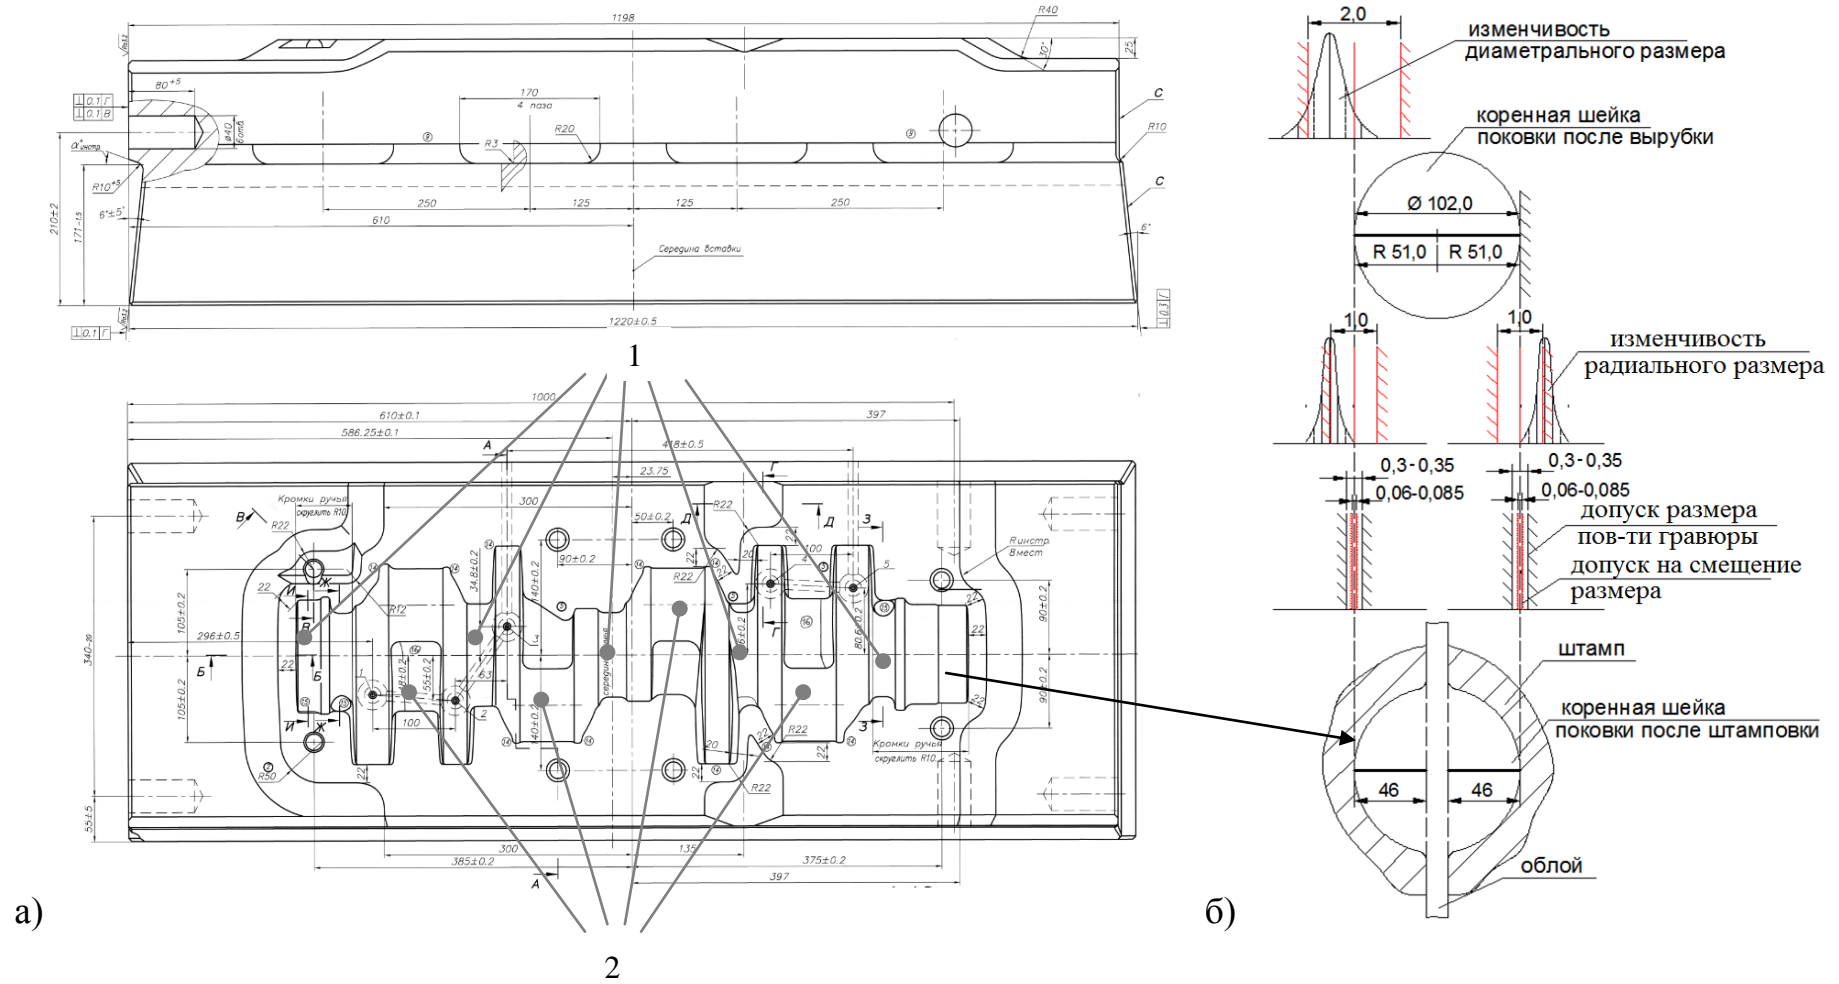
а) Нижний штамп горячей объемной штамповки поковки коленчатого вала, б) допуски изготовления коренной шейки поковки и положения профиля поверхности гравюры штампа 1 – поверхности гравюр коренных шеек, 2 – поверхности гравюр шатунных шеек
